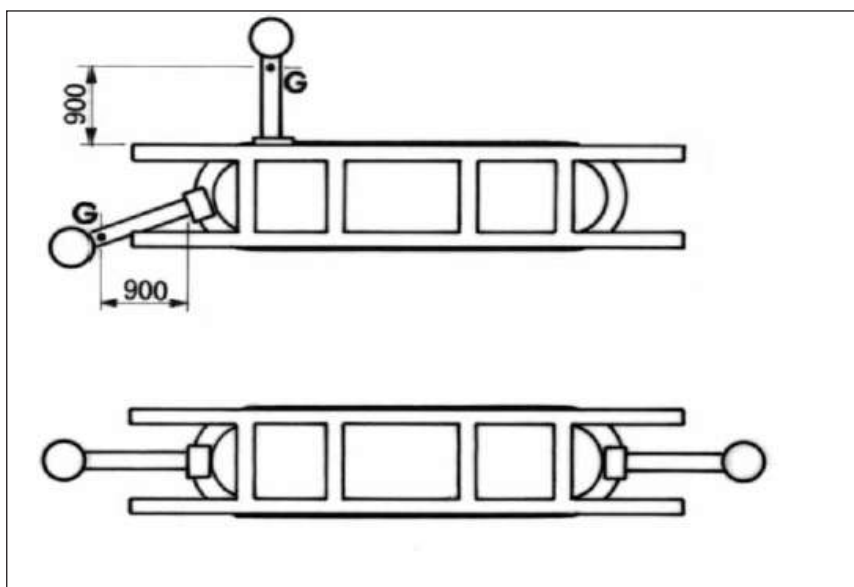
POSICIÓN DE MONTAJE DE LAS ELES SOBRE EL BANCO
